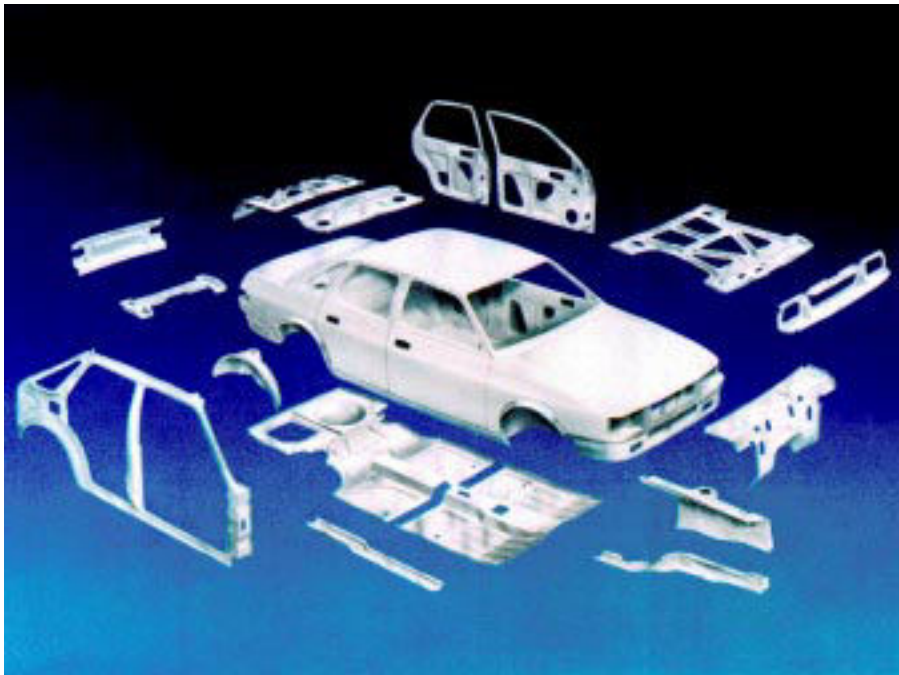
Blechteile einer Automobilkarosserie (Quelle: Soudronic)
